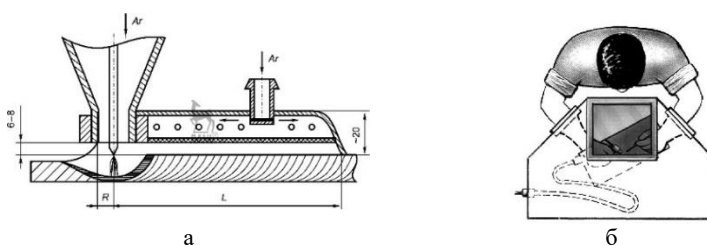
Способы защиты металла сварного соединения в процессе сварки титановых сплавов:
